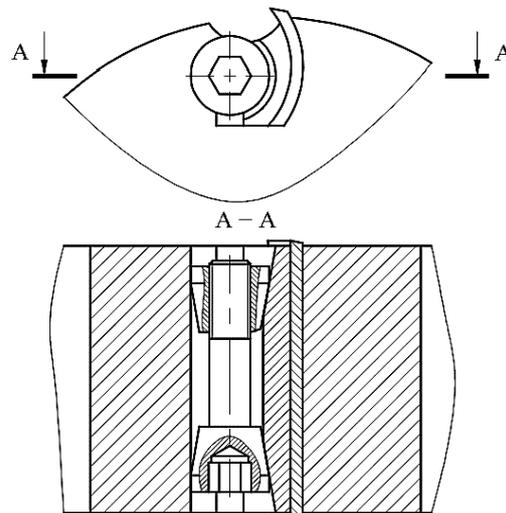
Узел крепления режущего ножа с осевым расположением винта
